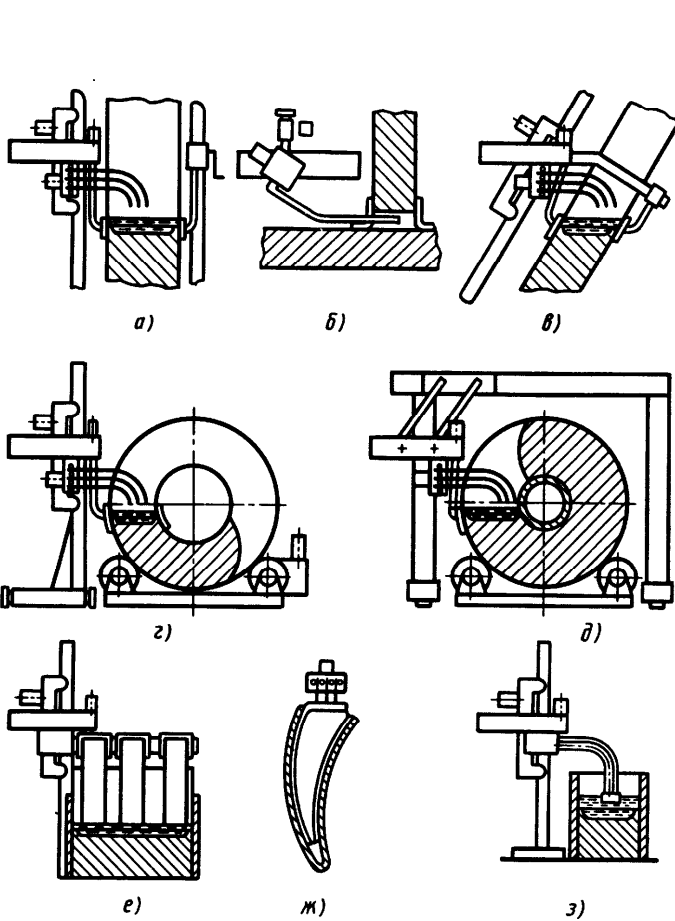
Схемы настроек аппарата А-535 для сварки различных швов и соединений
